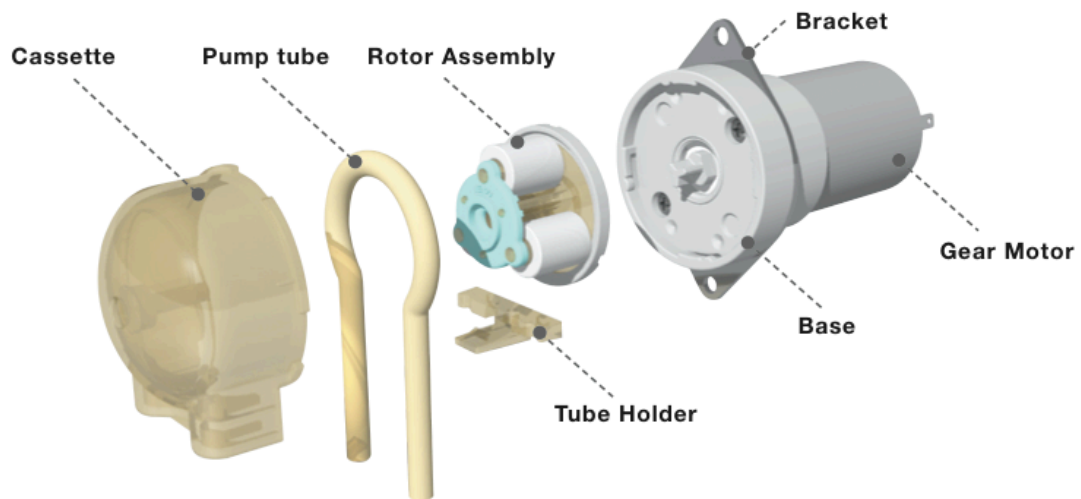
Immagine illustrativa dei componenti della pompa. Partendo da destra è visibile il motore, che può essere disassemblato dalla parte restante in polisulfone e dunque autoclavabile costituita da una parte rotante, il ferma-tubo, il sottopompa e il case.
